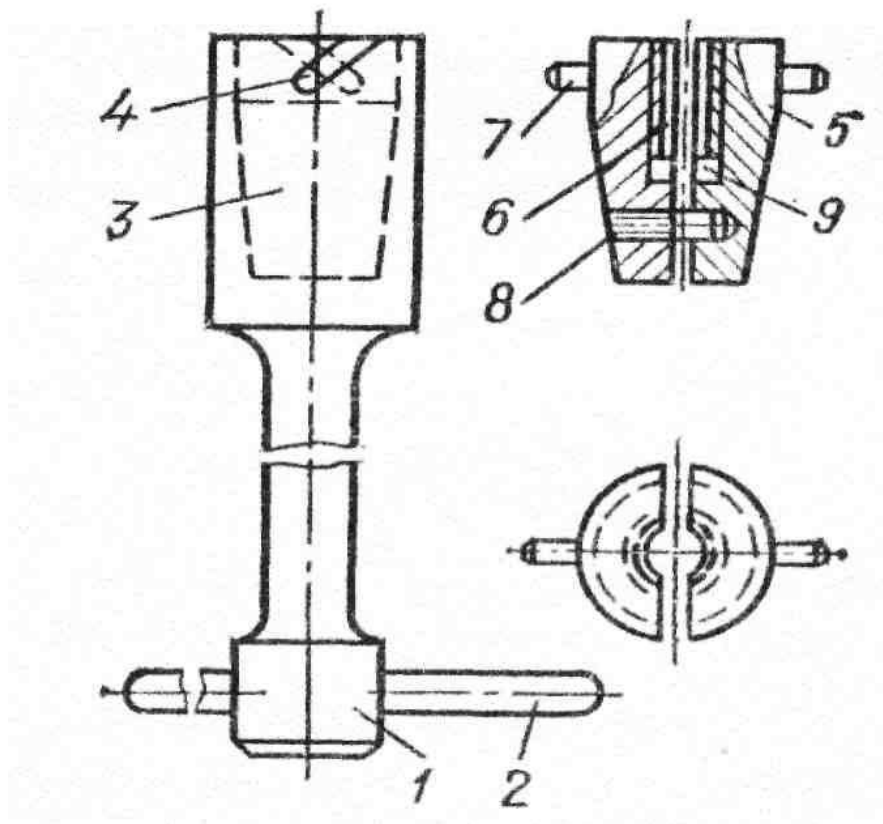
Пристрій з конічною розрізною гайкою: 1- стержень; 2- вороток; 3- головка; 4- проріз; 5- гайка; 6 і 8- шпильки; 7- штифт; 9- виточка.
